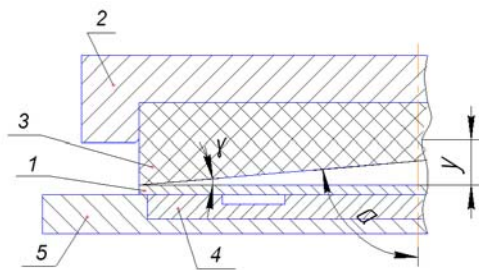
Конструктивная схема эластичной матрицы с внутренней конусностью в схеме с заделкой эластичной матрицы в полузамкнутом объеме: 1 - заготовка; 2 - силовая обойма; 3 - эластичная матрица; 4 - формообразующий инструмент; 5 - технологическая обойма
